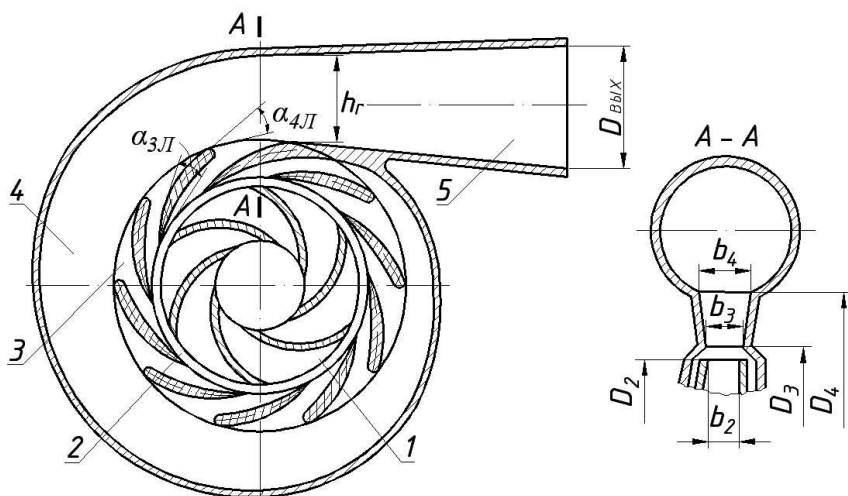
Отвод центробежного насоса: 1 – центробежное колесо; 2 – кольцевой безлопаточный диффузор; 3 – кольцевой лопаточный направляющий аппарат; 4 – спиральный сборник; 5 – прямой конический диффузор
